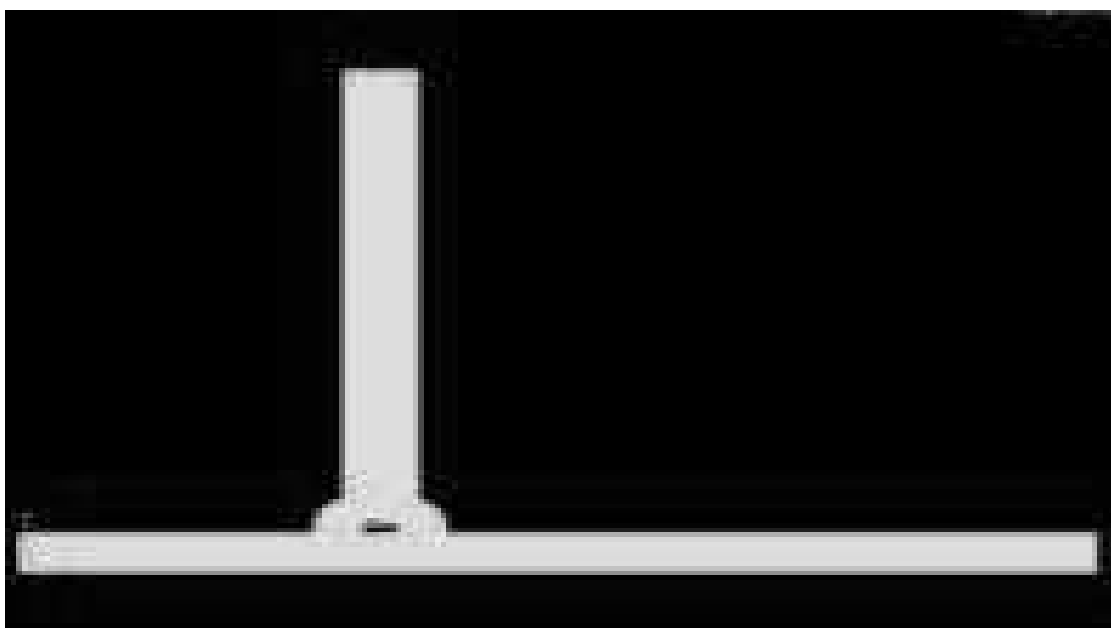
Фрагмент сварного соединения с выбранными элементами
